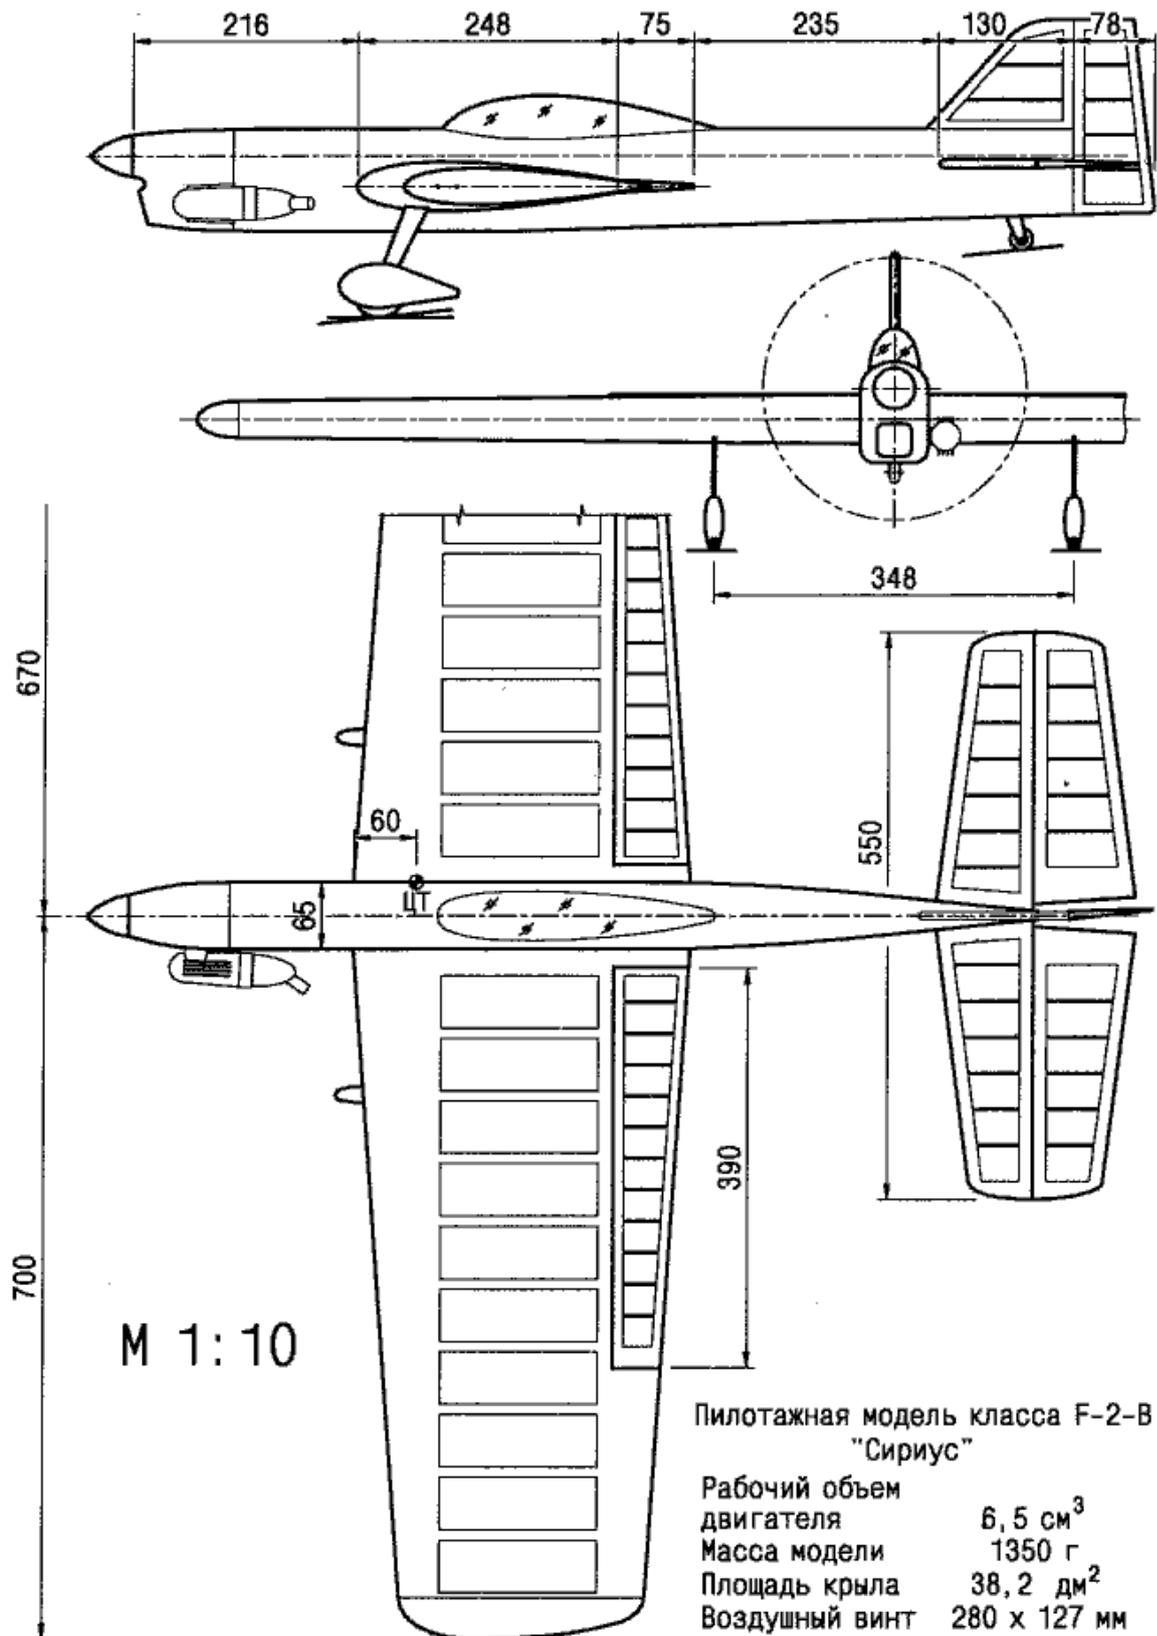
Чертёж кордовой модели F-2-B. Общий вид
